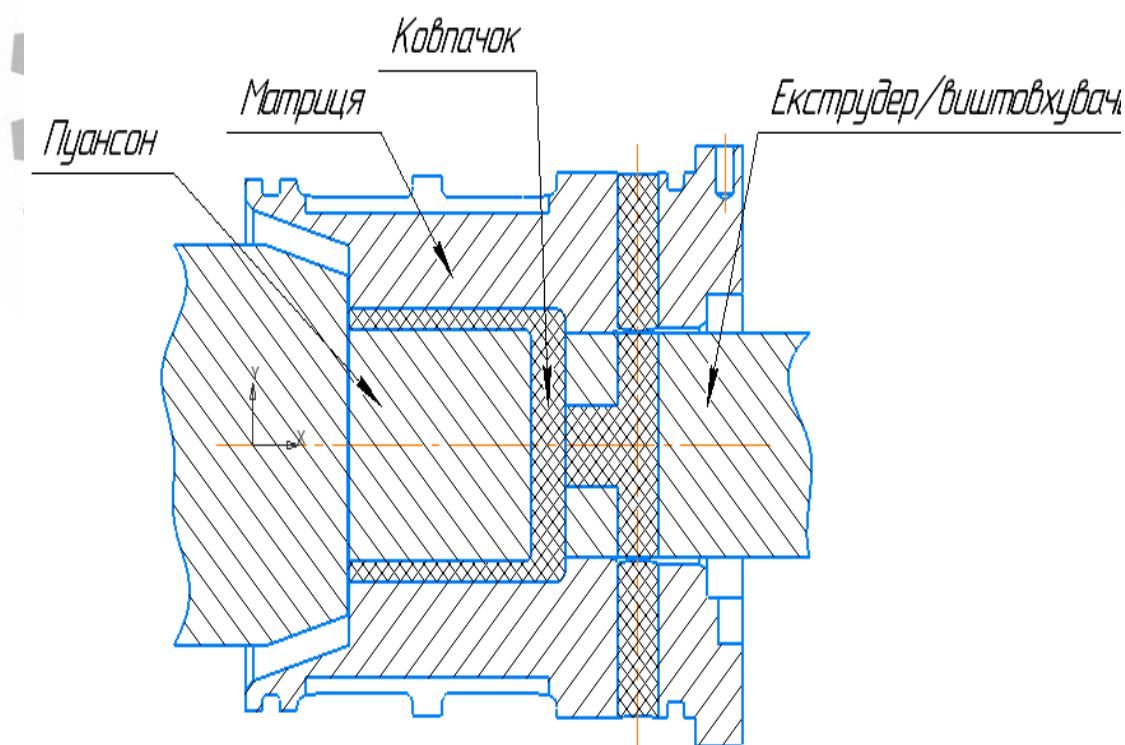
Ескіз виготовлення деталі «Ковпачок»
